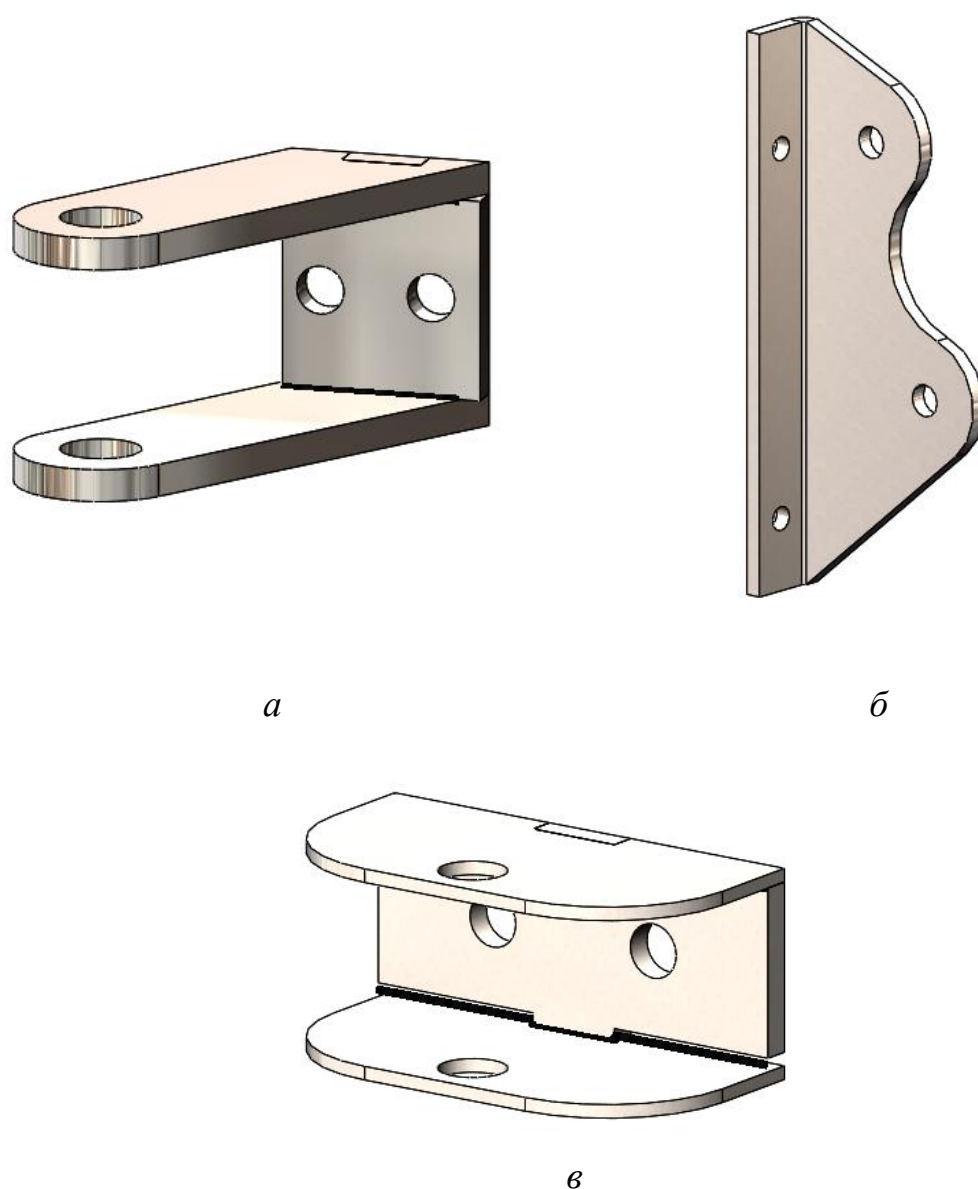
3D модели кронштейнов поворотного кулака: *а* – кронштейн крепления рулевой тяги; *б* – кронштейн крепления тормозного суппорта; *в* – кронштейн крепления верхнего рычага.
